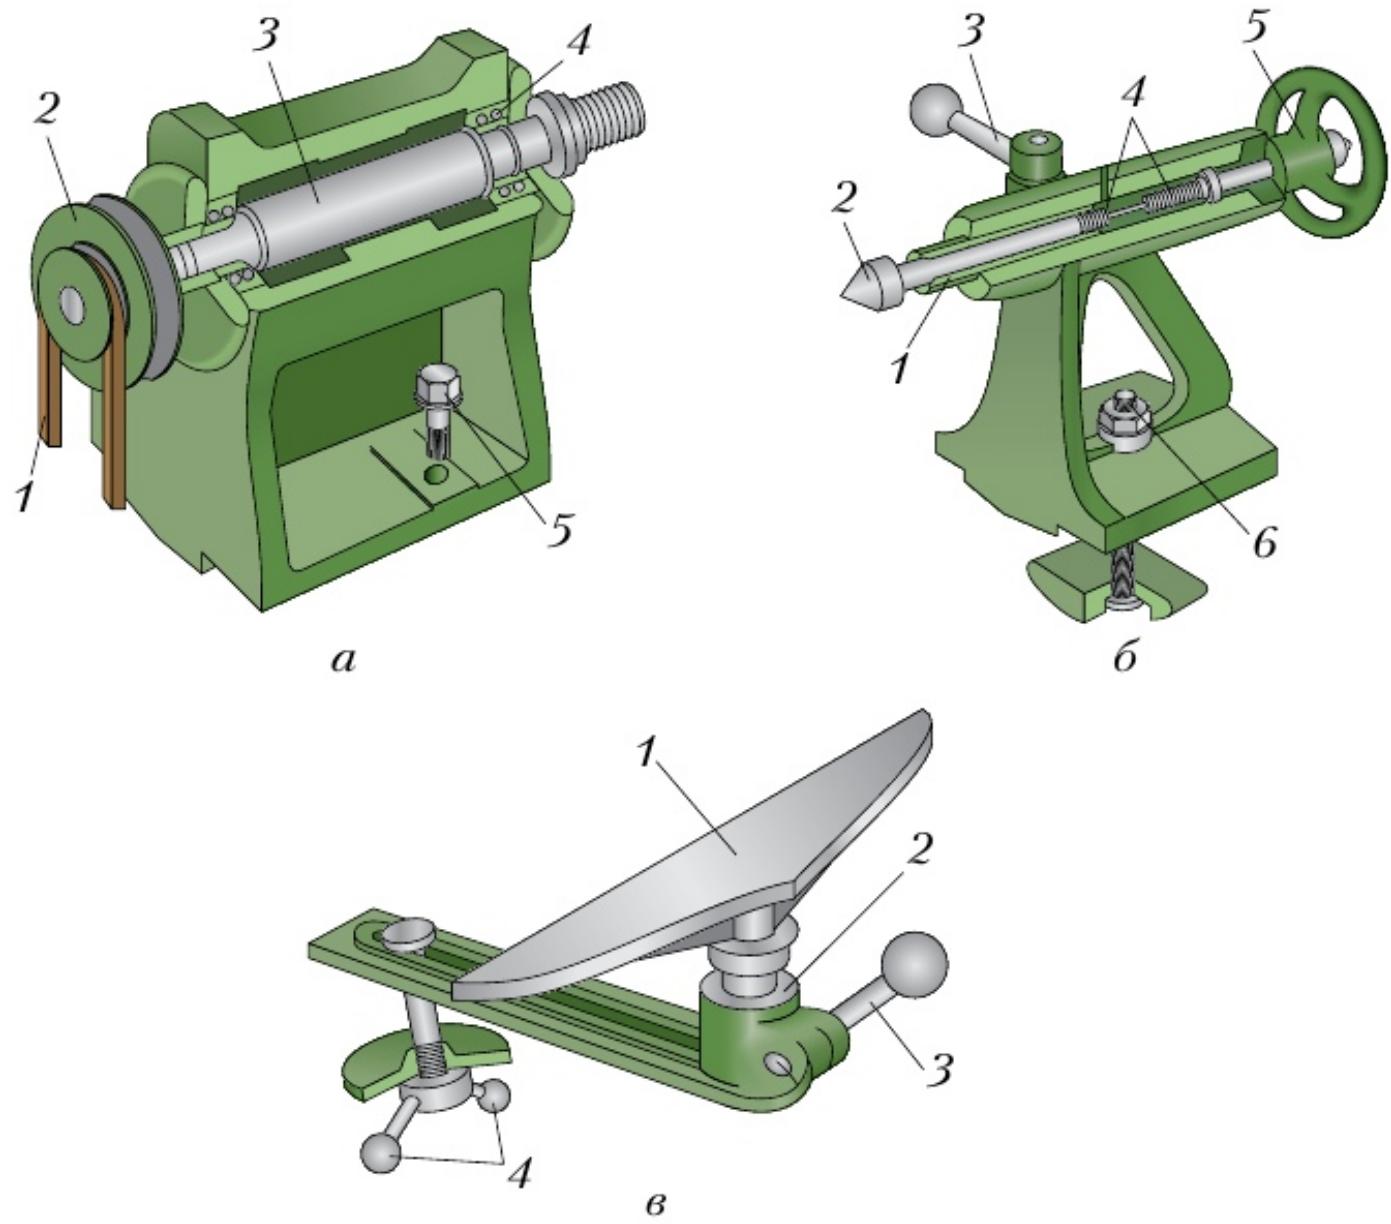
Основные части станка СТД-120М: а – передняя бабка: 1 – клиновой ремень ремённой передачи; 2 – двухступенчатый шкив; 3 – шпиндель; 4 – подшипник шариковый; 5 – крепёжный винт; б – задняя бабка: 1 – пиноль; 2 – центр; 3 – рукоятка зажима; 4 – винтовой механизм; 5 – маховик; 6 – крепёжный болт; в – подручник в сборе: 1 – подручник; 2 – каретка (держатель); 3 – рукоятка стопора; 4 – рукоятки крепления каретки
